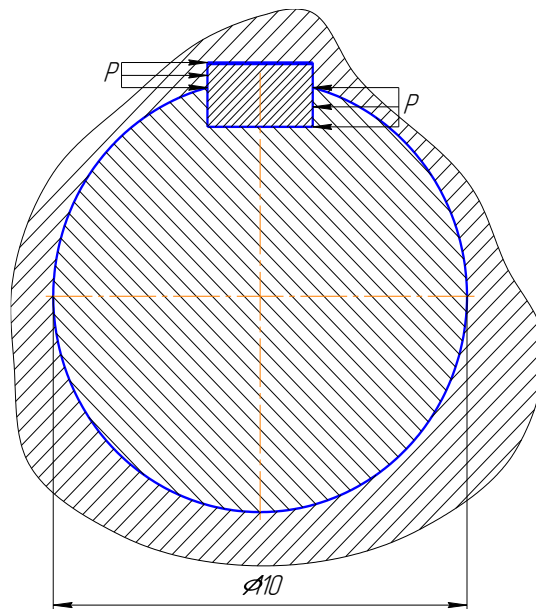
Розрахункова схема шпонкового з'єднання в місці кріплення вала з маточиною барабана
